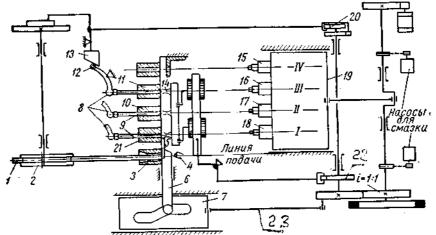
Кинематическая схема пресса-автомата модели А411 для штамповки гаек
